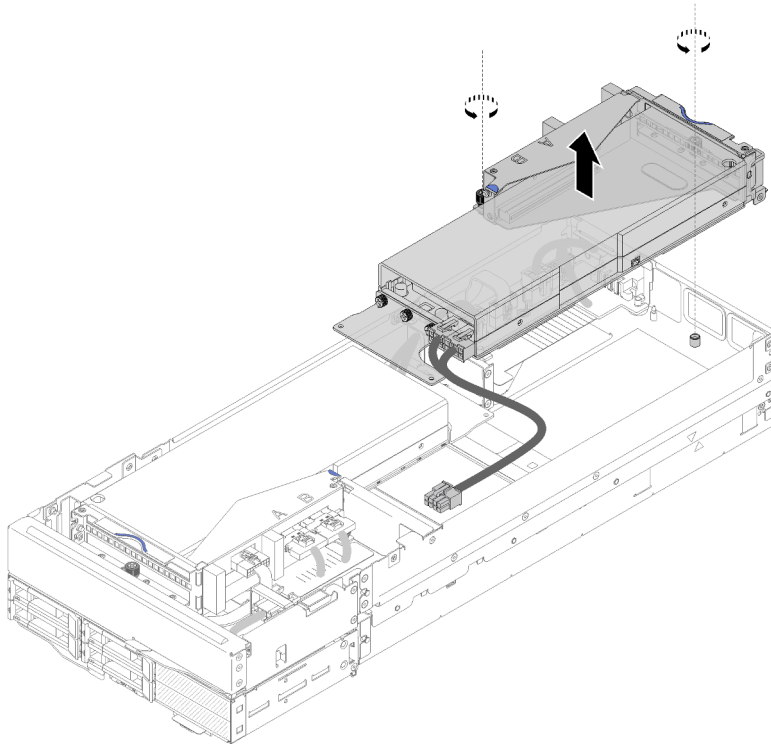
Retrait de l'assemblage de cartes mezzanines arrière du nœud d'extension
